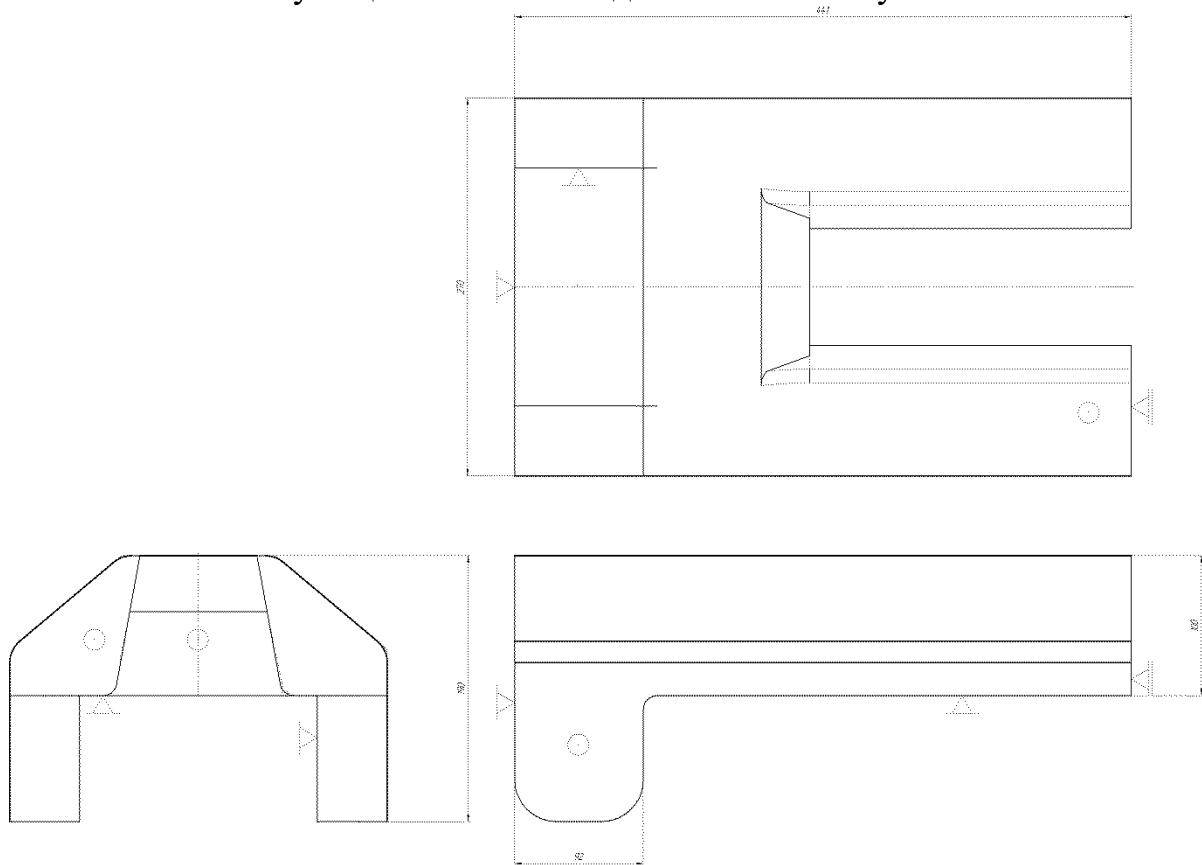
Умовна схема базування на фрезерній операції, установ А
